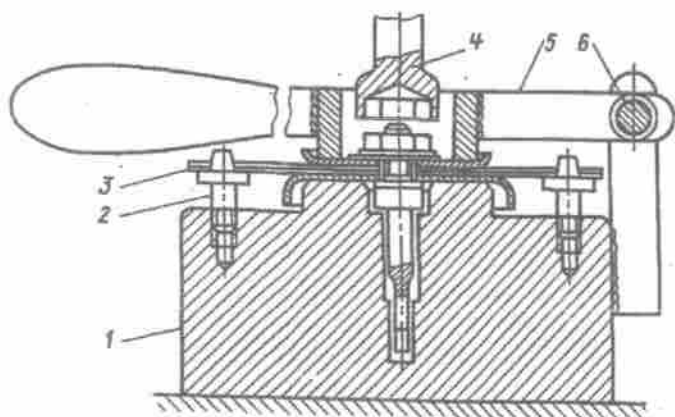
Vorrichtung zum Zusammenbau der Kraftstoffpumpenmembran:
